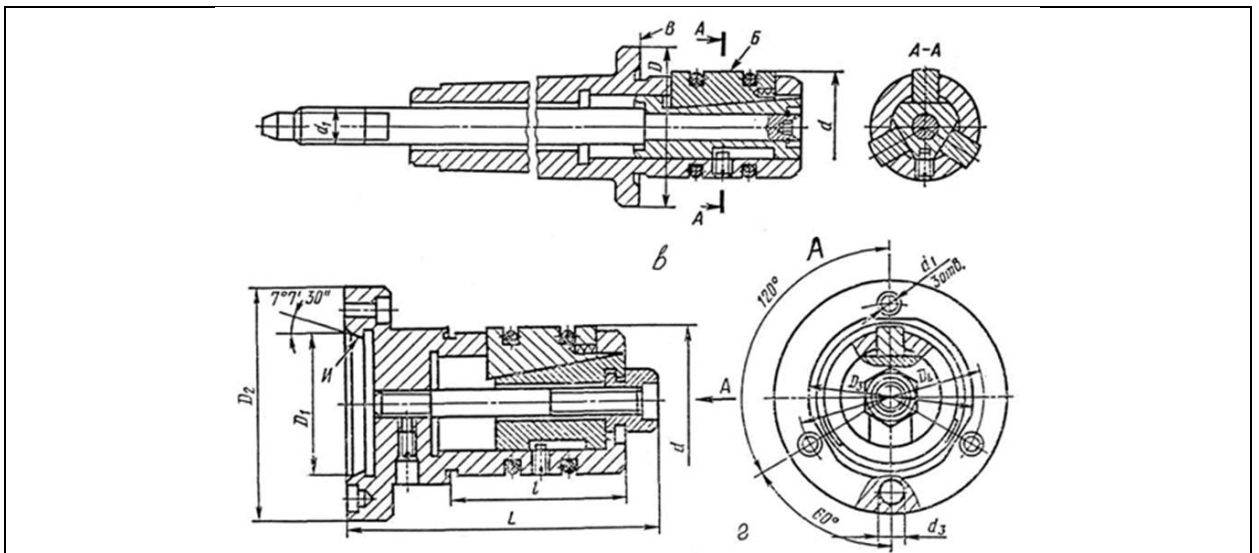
Приклади конструкцій клинокулачкових оправок
